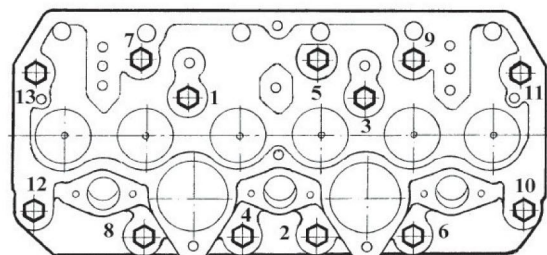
Схема последовательности затяжки болтов крепления головки цилиндров
